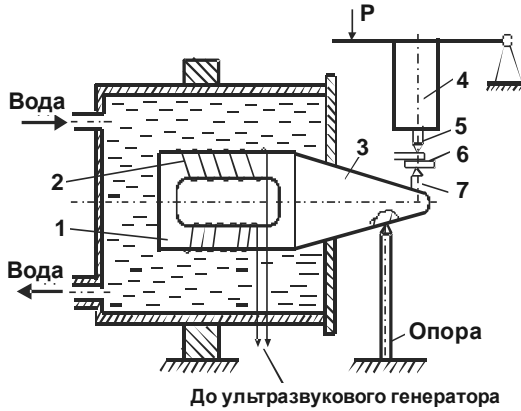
Схема установки для точкового зварювання ультразвуком
